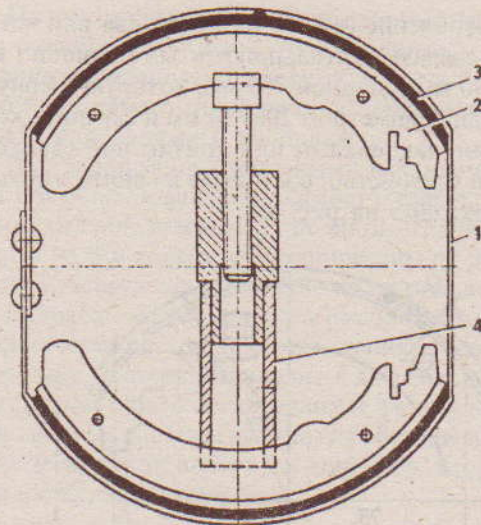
Приспособление для приклейки накладок тормозных колодок: 1 - стальная лента; 2 - колодка; 3 - накладка; 4 - разжимное устройство
